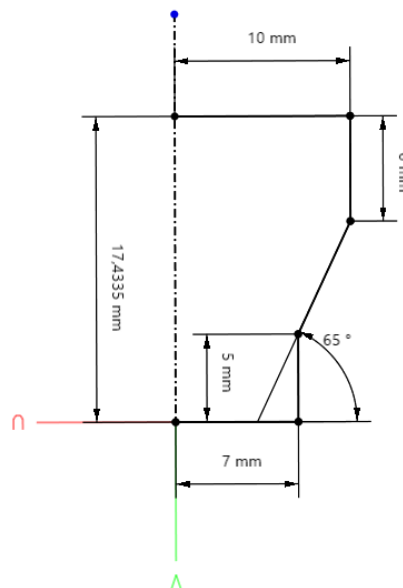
Imagen de las dimensiones geométricas exteriores de la pieza 6 antes de realizar el diseño de los dientes.
